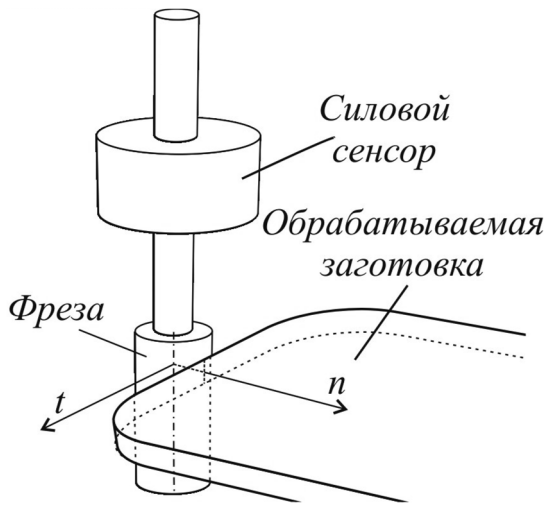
Обобщенная схема движения манипулятора вдоль боковой поверхности заготовки
